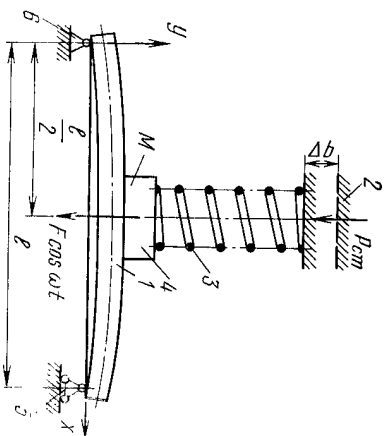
Схема нагружения образца для исправления деформаций продольного изгиба: 1 — образец; 2 — нагружающее устройство; 3 — упругий элемент; 4 — вибратор; 5 — подвижная опора; 6 — неподвижная опора.
